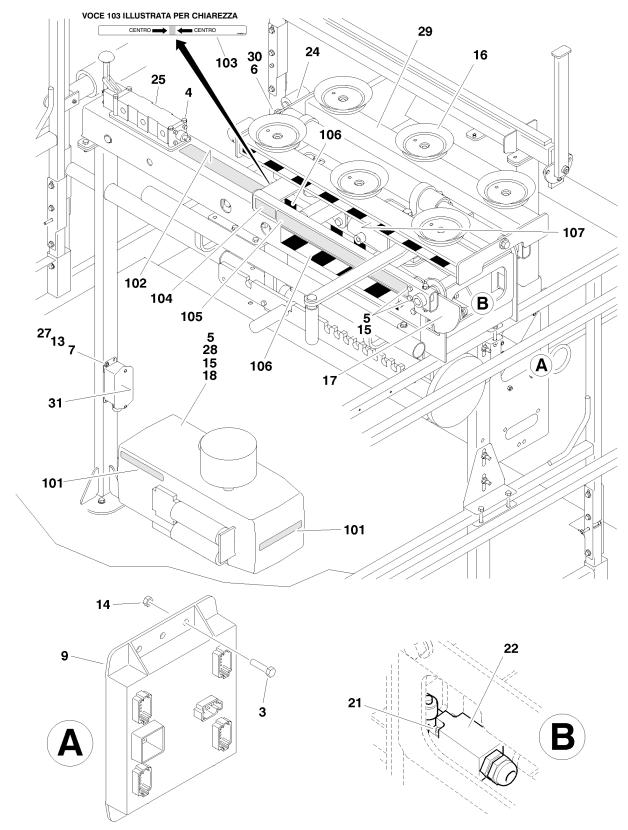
Disegno dei componenti dei bracci vuoto di Easi-Cladder™ Plus
